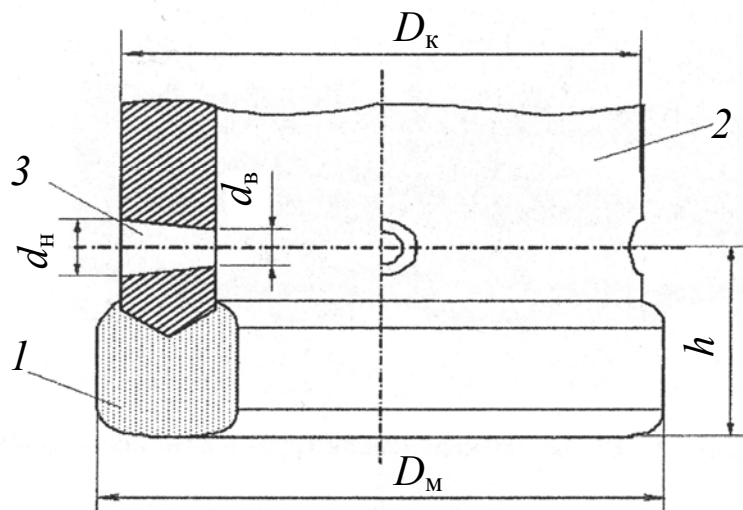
Коронка с конусными промывочными каналами: 1 – матрица; 2 – корпус коронки; 3 – промывочный канал;  $D_M$ ,  $D_K$  – наружные диаметры матрицы и коронки;  $d_H$  – наружный диаметр отверстия;  $d_B$  – внутренний диаметр отверстия;  $h$  – расстояние от торца матрицы до осевой линии промывочных каналов
